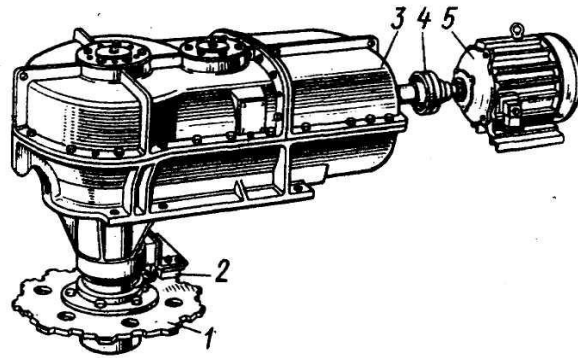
кутовий привід Редуктора підвісного конвейєра
